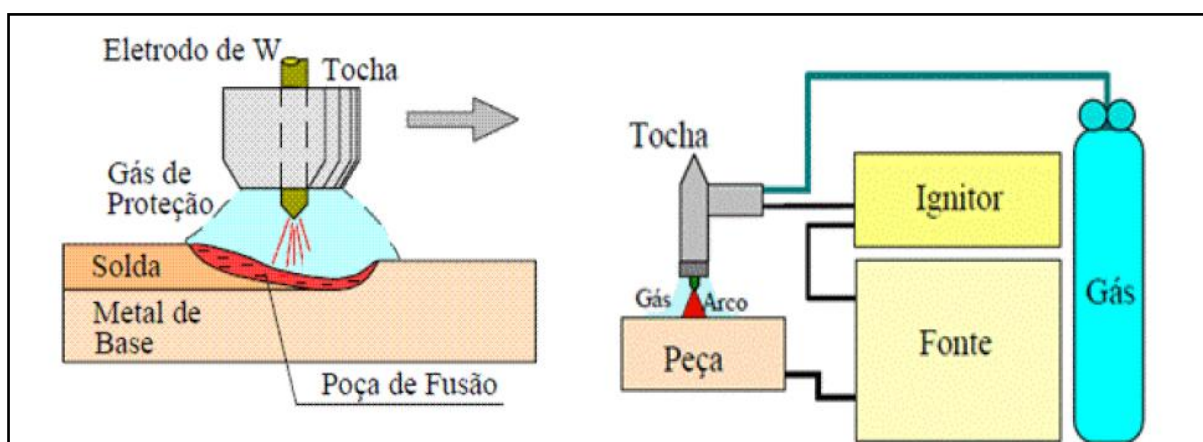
Região do arco e equipamento básico para soldagem GTAW (adaptação de MODENESI 2000)
